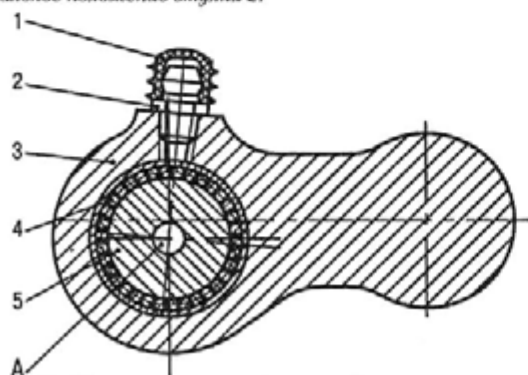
Шарнирное резьбовое соединение в верхней бобышке стойки подвески:
